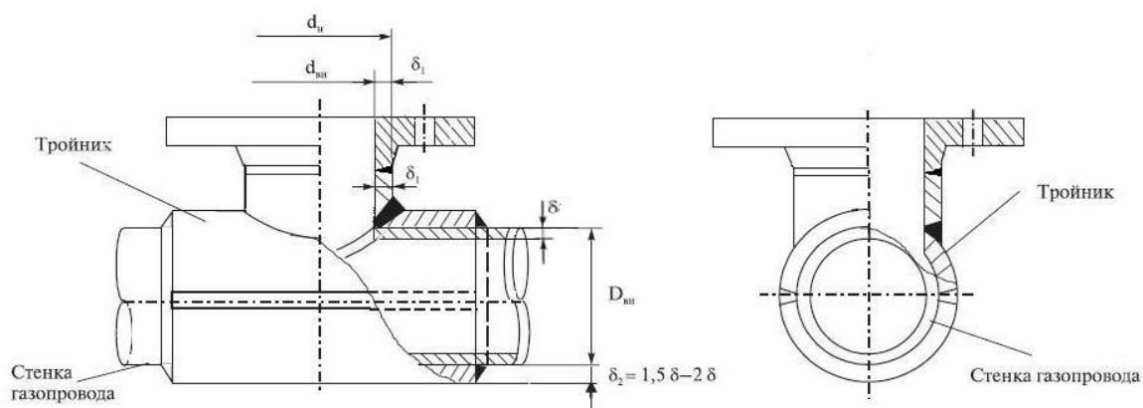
Тип IV тройник сварной с фланцем
